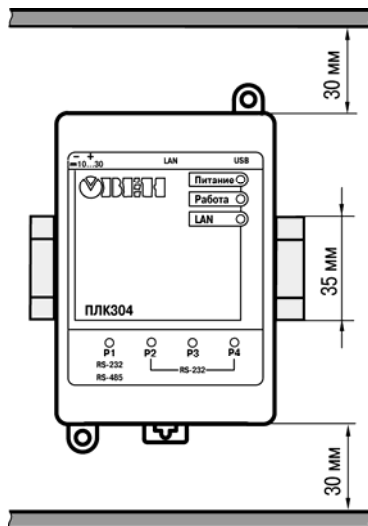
Расстояние до стенок корпуса ПЛК304 при монтаже для обеспечения вентиляции
